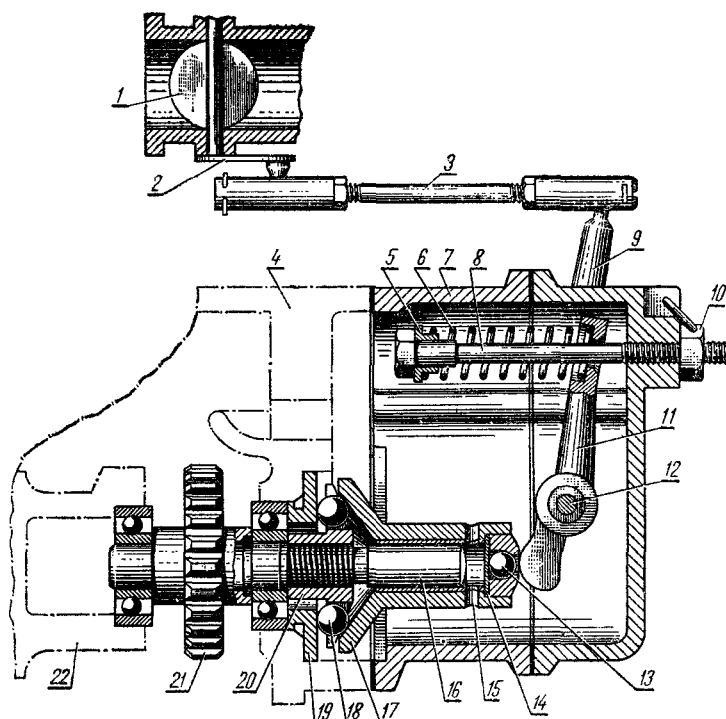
Однорежимный шариковый центробежный регулятор пускового двигателя ПД-10У:
